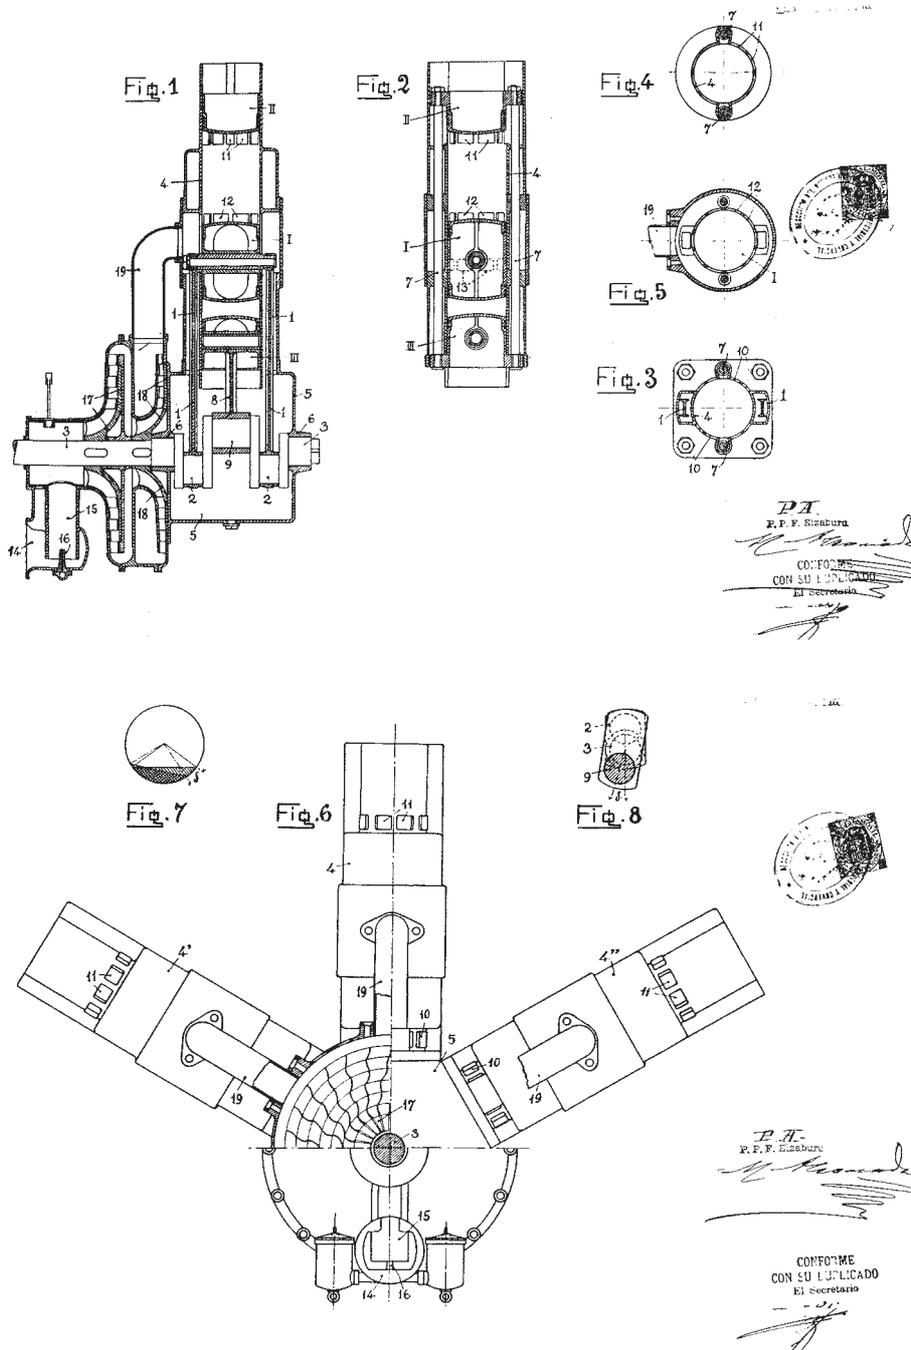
Dibujos del motor sobrealimentado de Zoller, patente ES 49 638 de 1911 (OEPM, Madrid)
